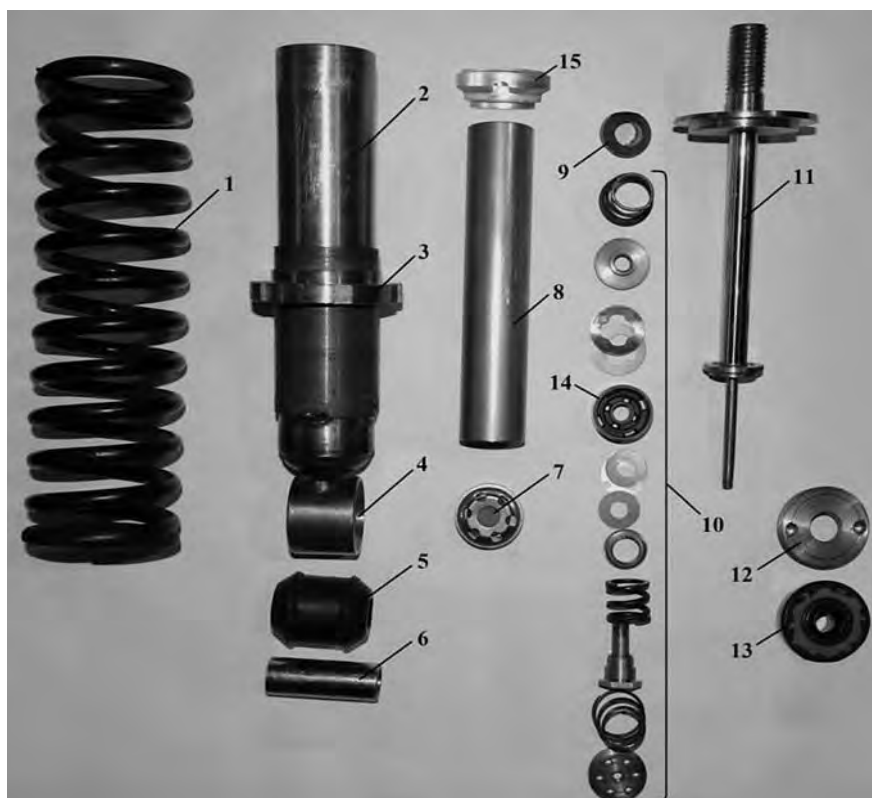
Конструкция опытного демпфера кабины колесного трактора: 1 – цилиндрическая пружина; 2 – резервуар амортизатора в сборе; 3 – гайка пружины; 4 – проушина; 5 – резиновая втулка; 6 – втулка шарнира; 7 – клапан сжатия в сборе; 8 – цилиндр; 9 – буфер хода отбоя; 10 – детали поршневого узла; 11 – шток в сборе; 12 – гайка резервуара; 13 – сальник штока; 14 – поршень; 15 – направляющая втулка
